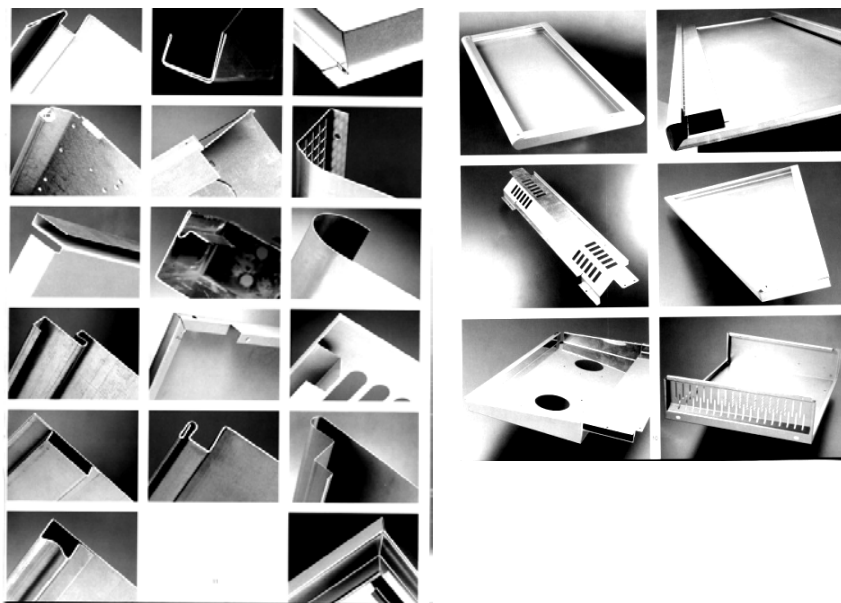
Образцы деталей, обрабатываемых на листогибочном оборудовании FINN-POWER
